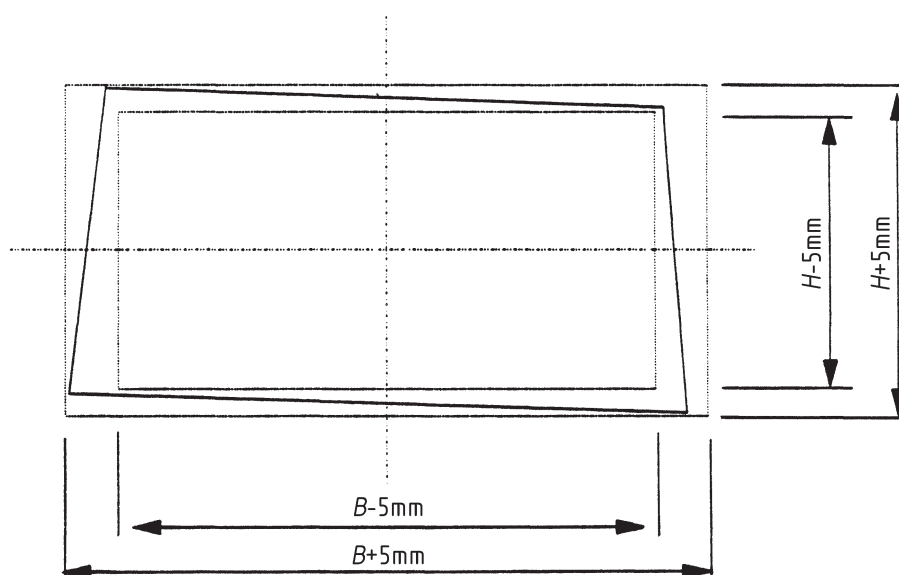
Ermittlung von Länge, Breite und Rechtwinkligkeit bei Lager-/Standardmaßen
